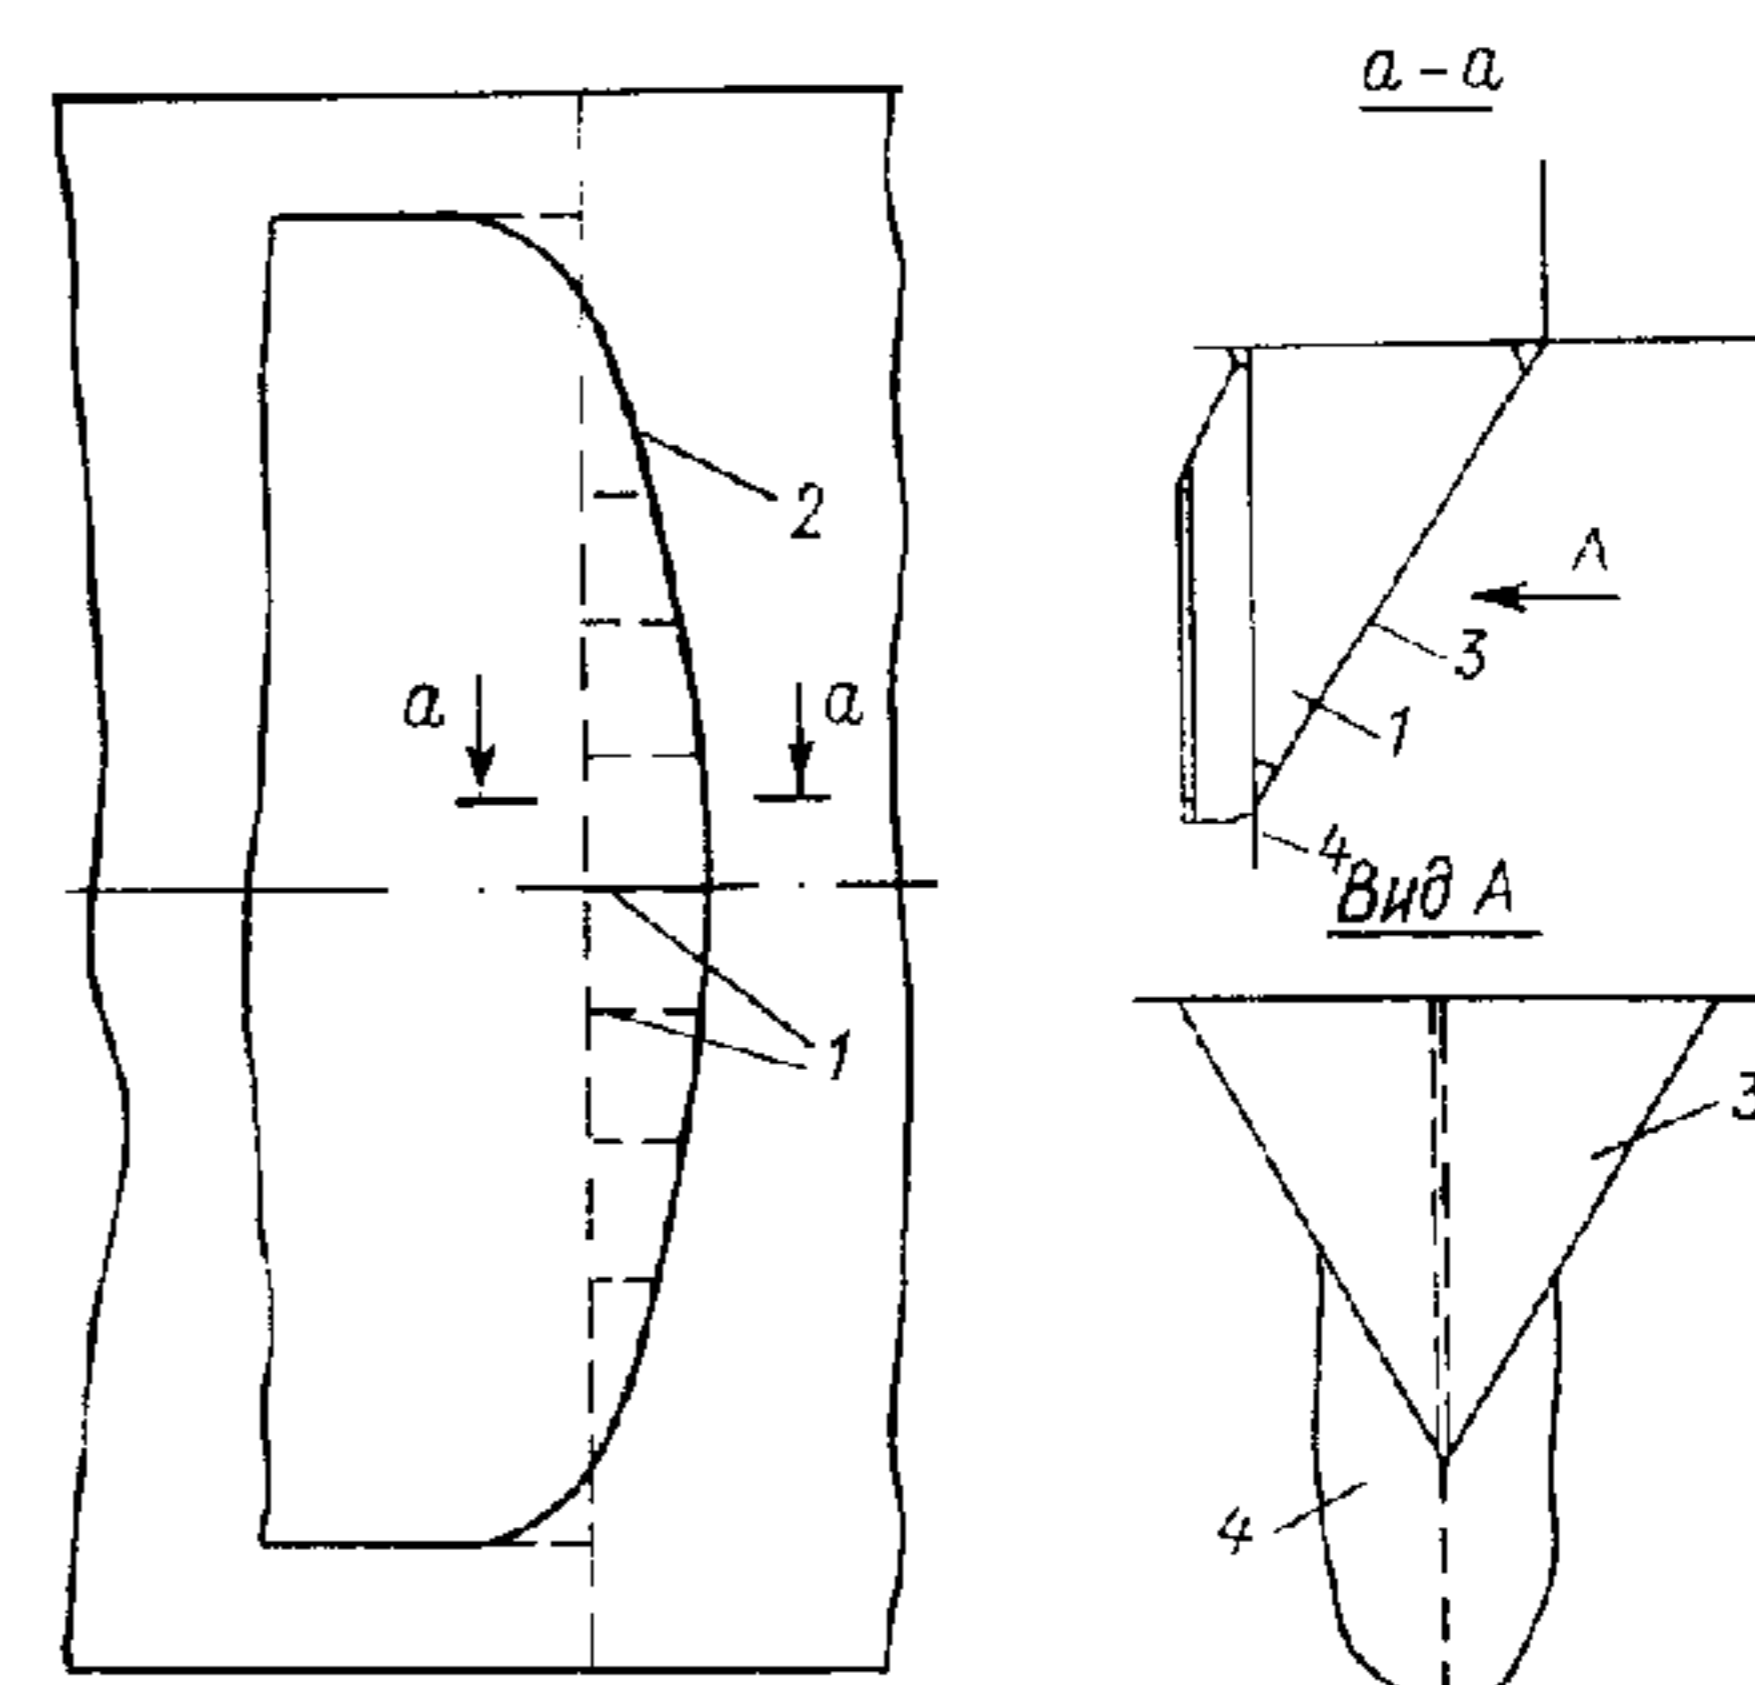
Перевязка носовой переборки надстройки с поперечной переборкой корпуса:
